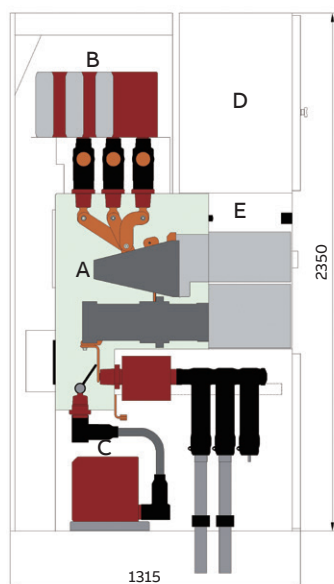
Vývodové pole s kabelem 1250 A (instalace u stěny)
